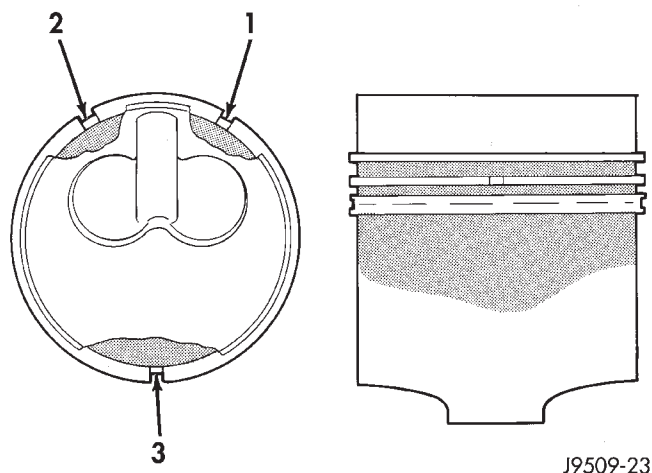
Emplazamiento de entrehierros de aro de pistón
